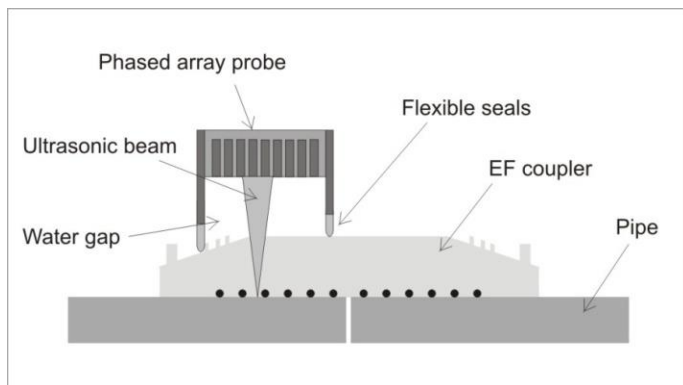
ESQUEMA DE LA TÉCNICA DE INSPECCIÓN PARA UNIONES POR EF
